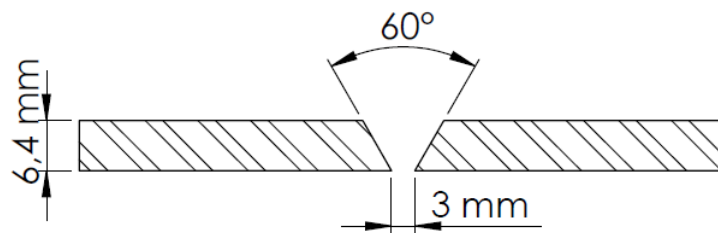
Dimensões da junta utilizada na etapa 1 para a avaliação por soldagem dos corpos-de-prova.
